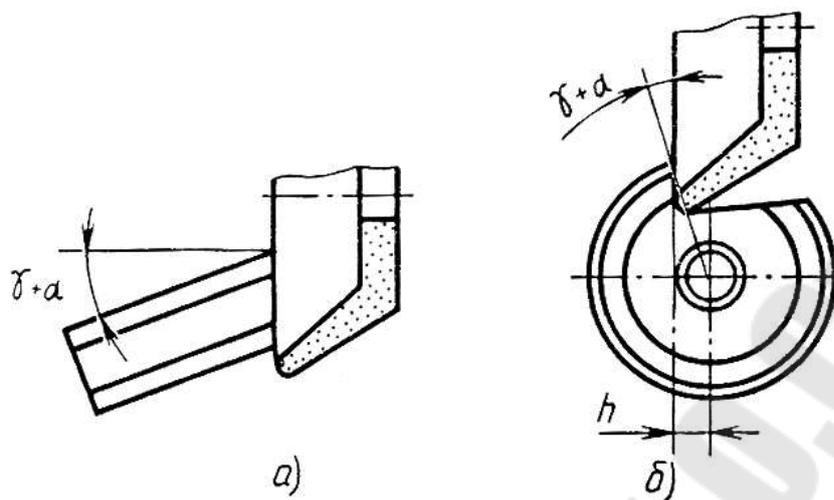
Схемы заточки фасонных резцов по передней поверхности: а – призматического; б – круглого.
